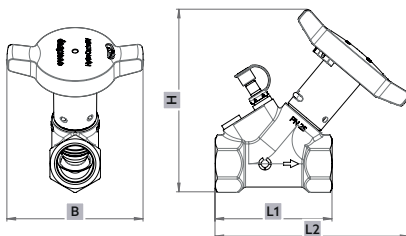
Размеры Вид сбоку / Вид спереди Внутренняя резьба
